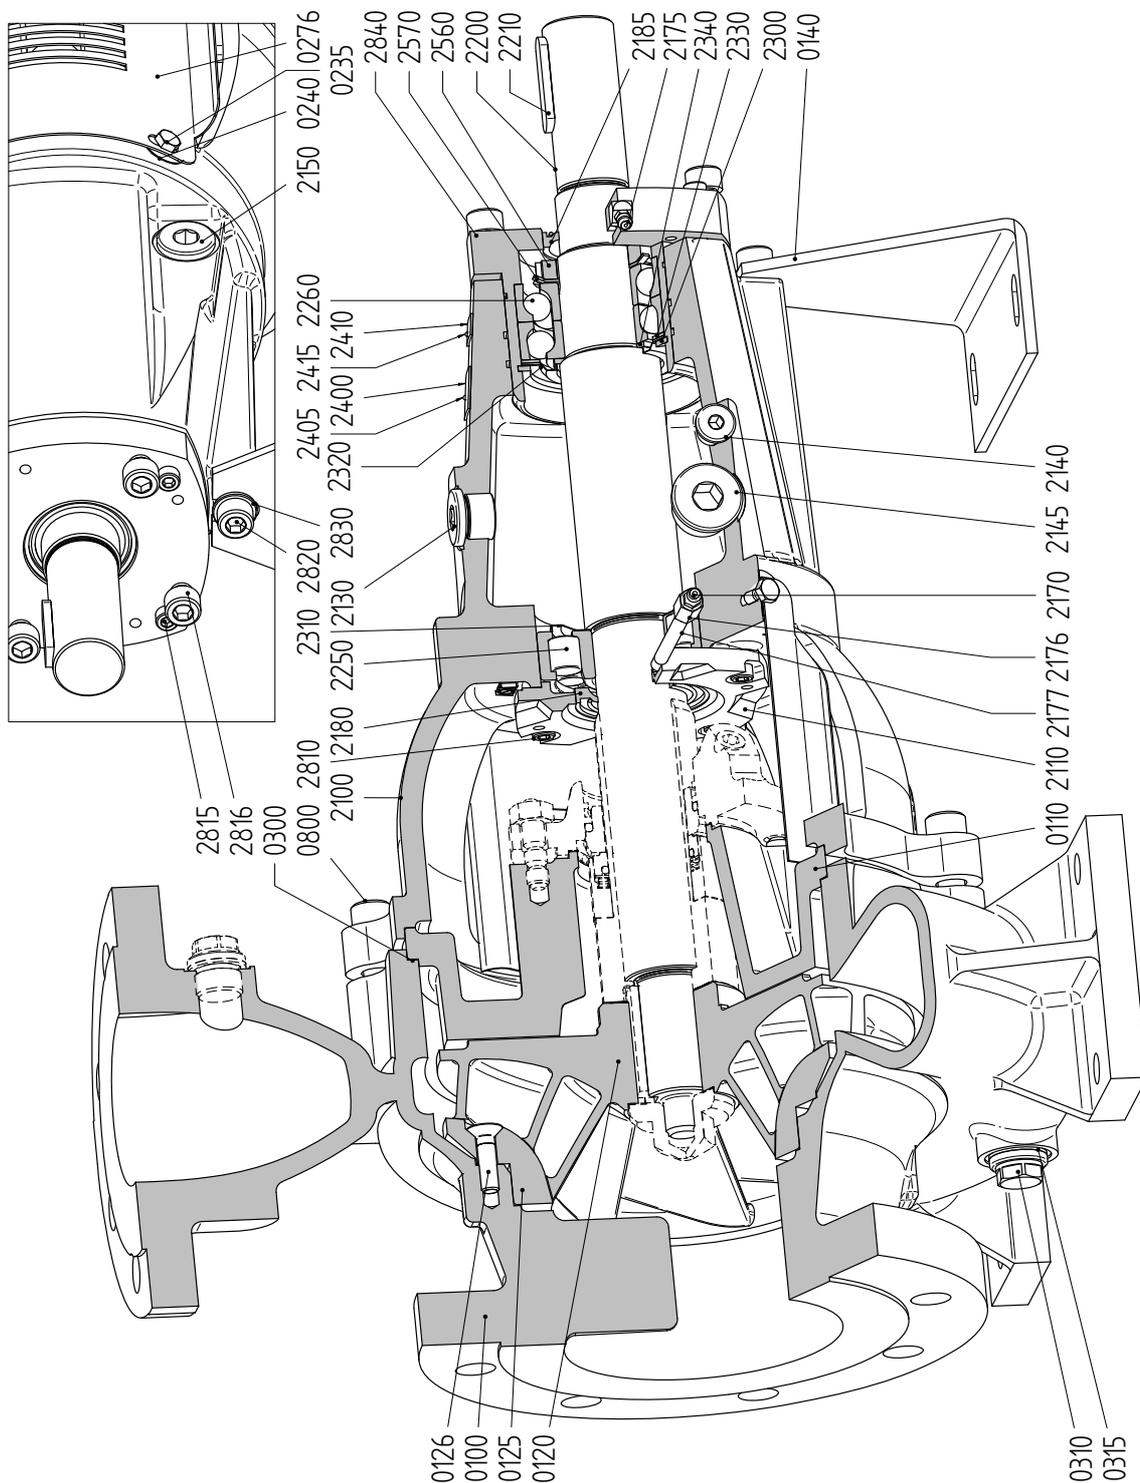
Чертеж в разрезе L5 с коническим отверстием
